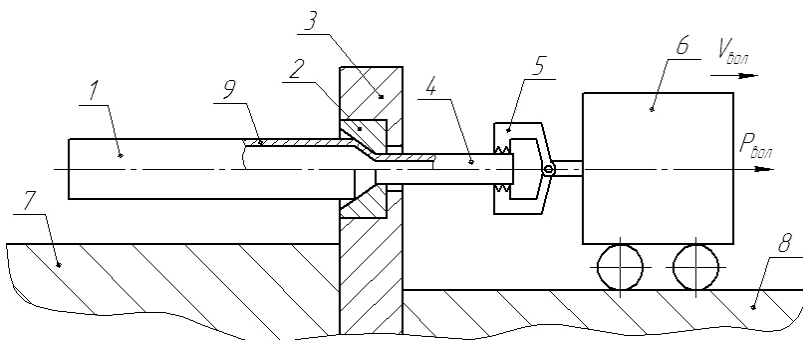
Схема безправочного волочения труб на волочильном стане: 1 – заготовка; 2 – волока; 3 – волокодержатель; 4 – захватка; 5 – клещи; 6 – тележка; 7 – загрузочный стол; 8 – станина; 9 – стенка трубы
